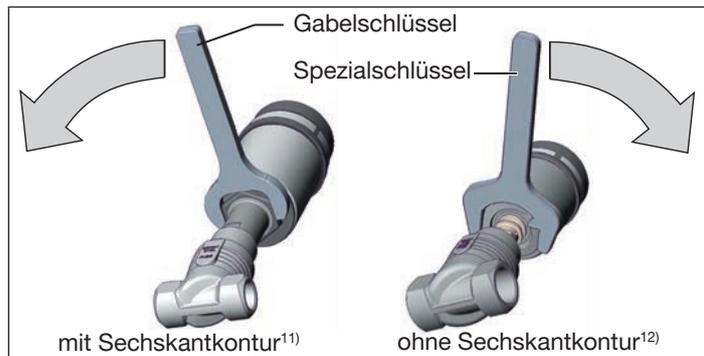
Drehen mit Gabelschlüssel / Spezialschlüssel
